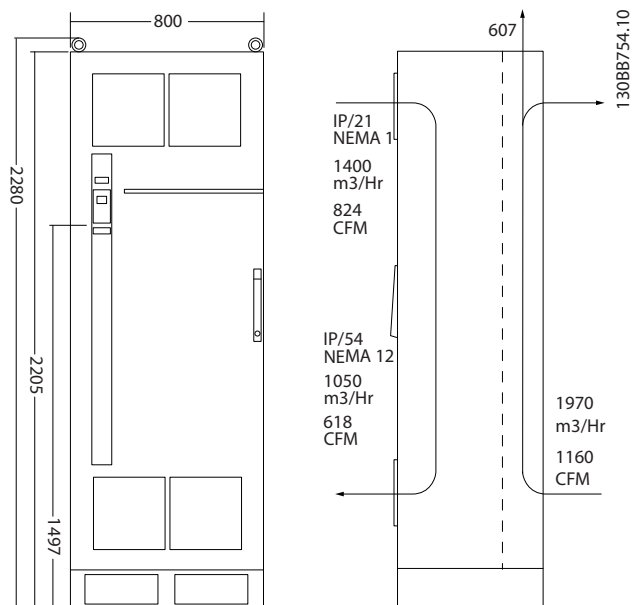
Dimensões Mecânicas (mm), F8
